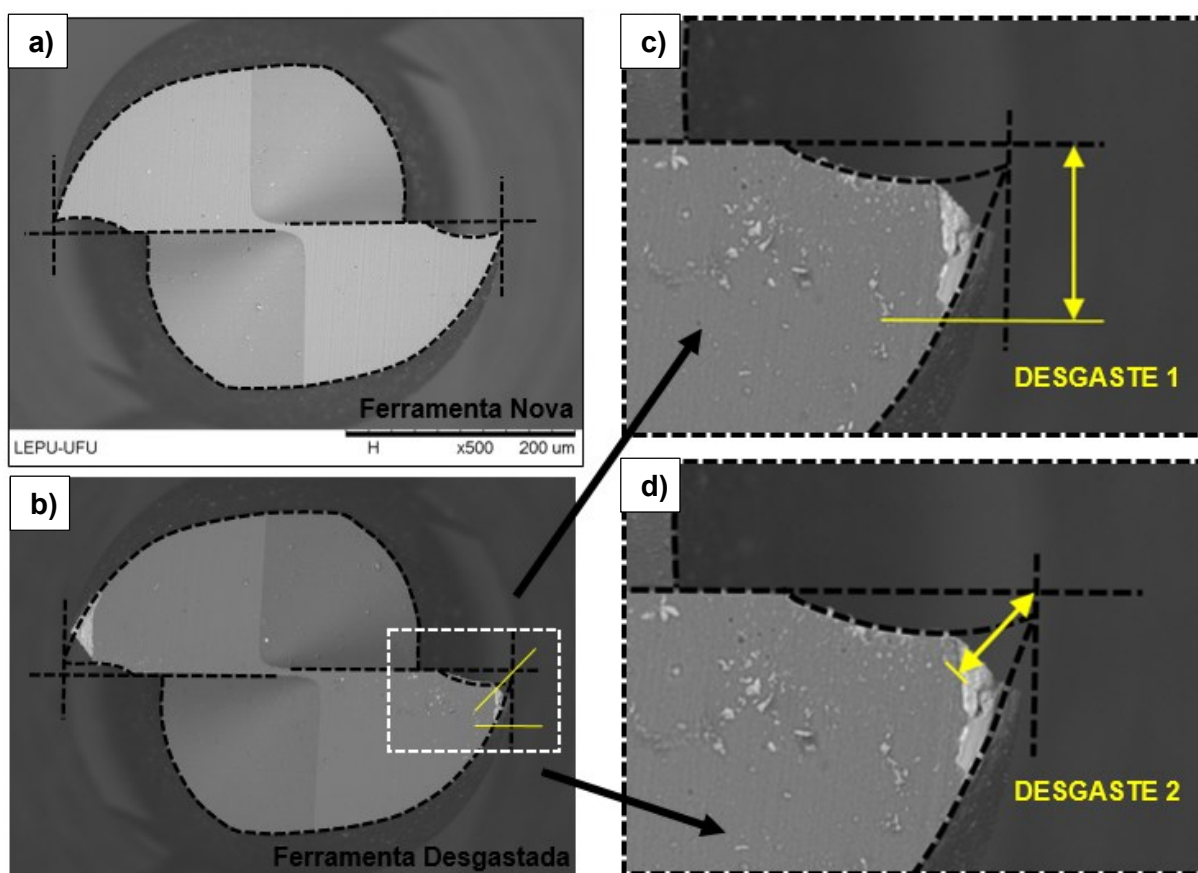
Detalhamento da medição do desgaste da ferramenta
